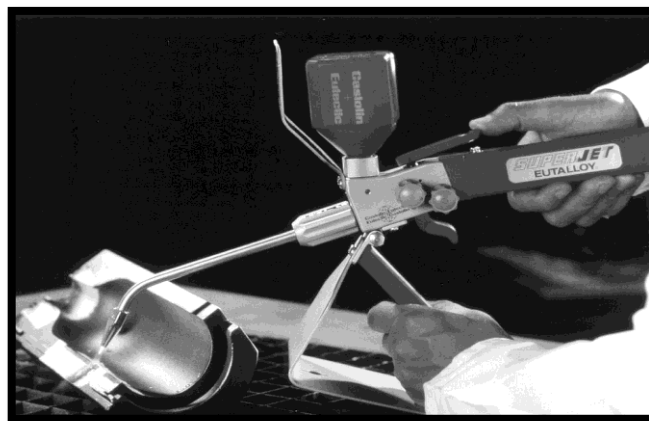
Projection flamme-poudre sur moule de verrerie
